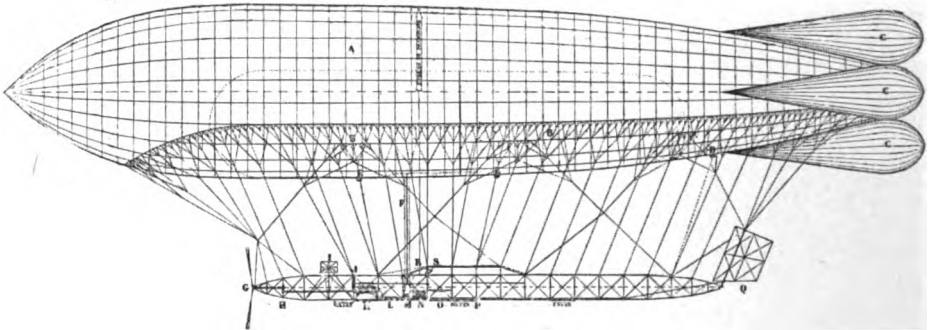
Plan des Clément-Bayard-Luftschiffes.
